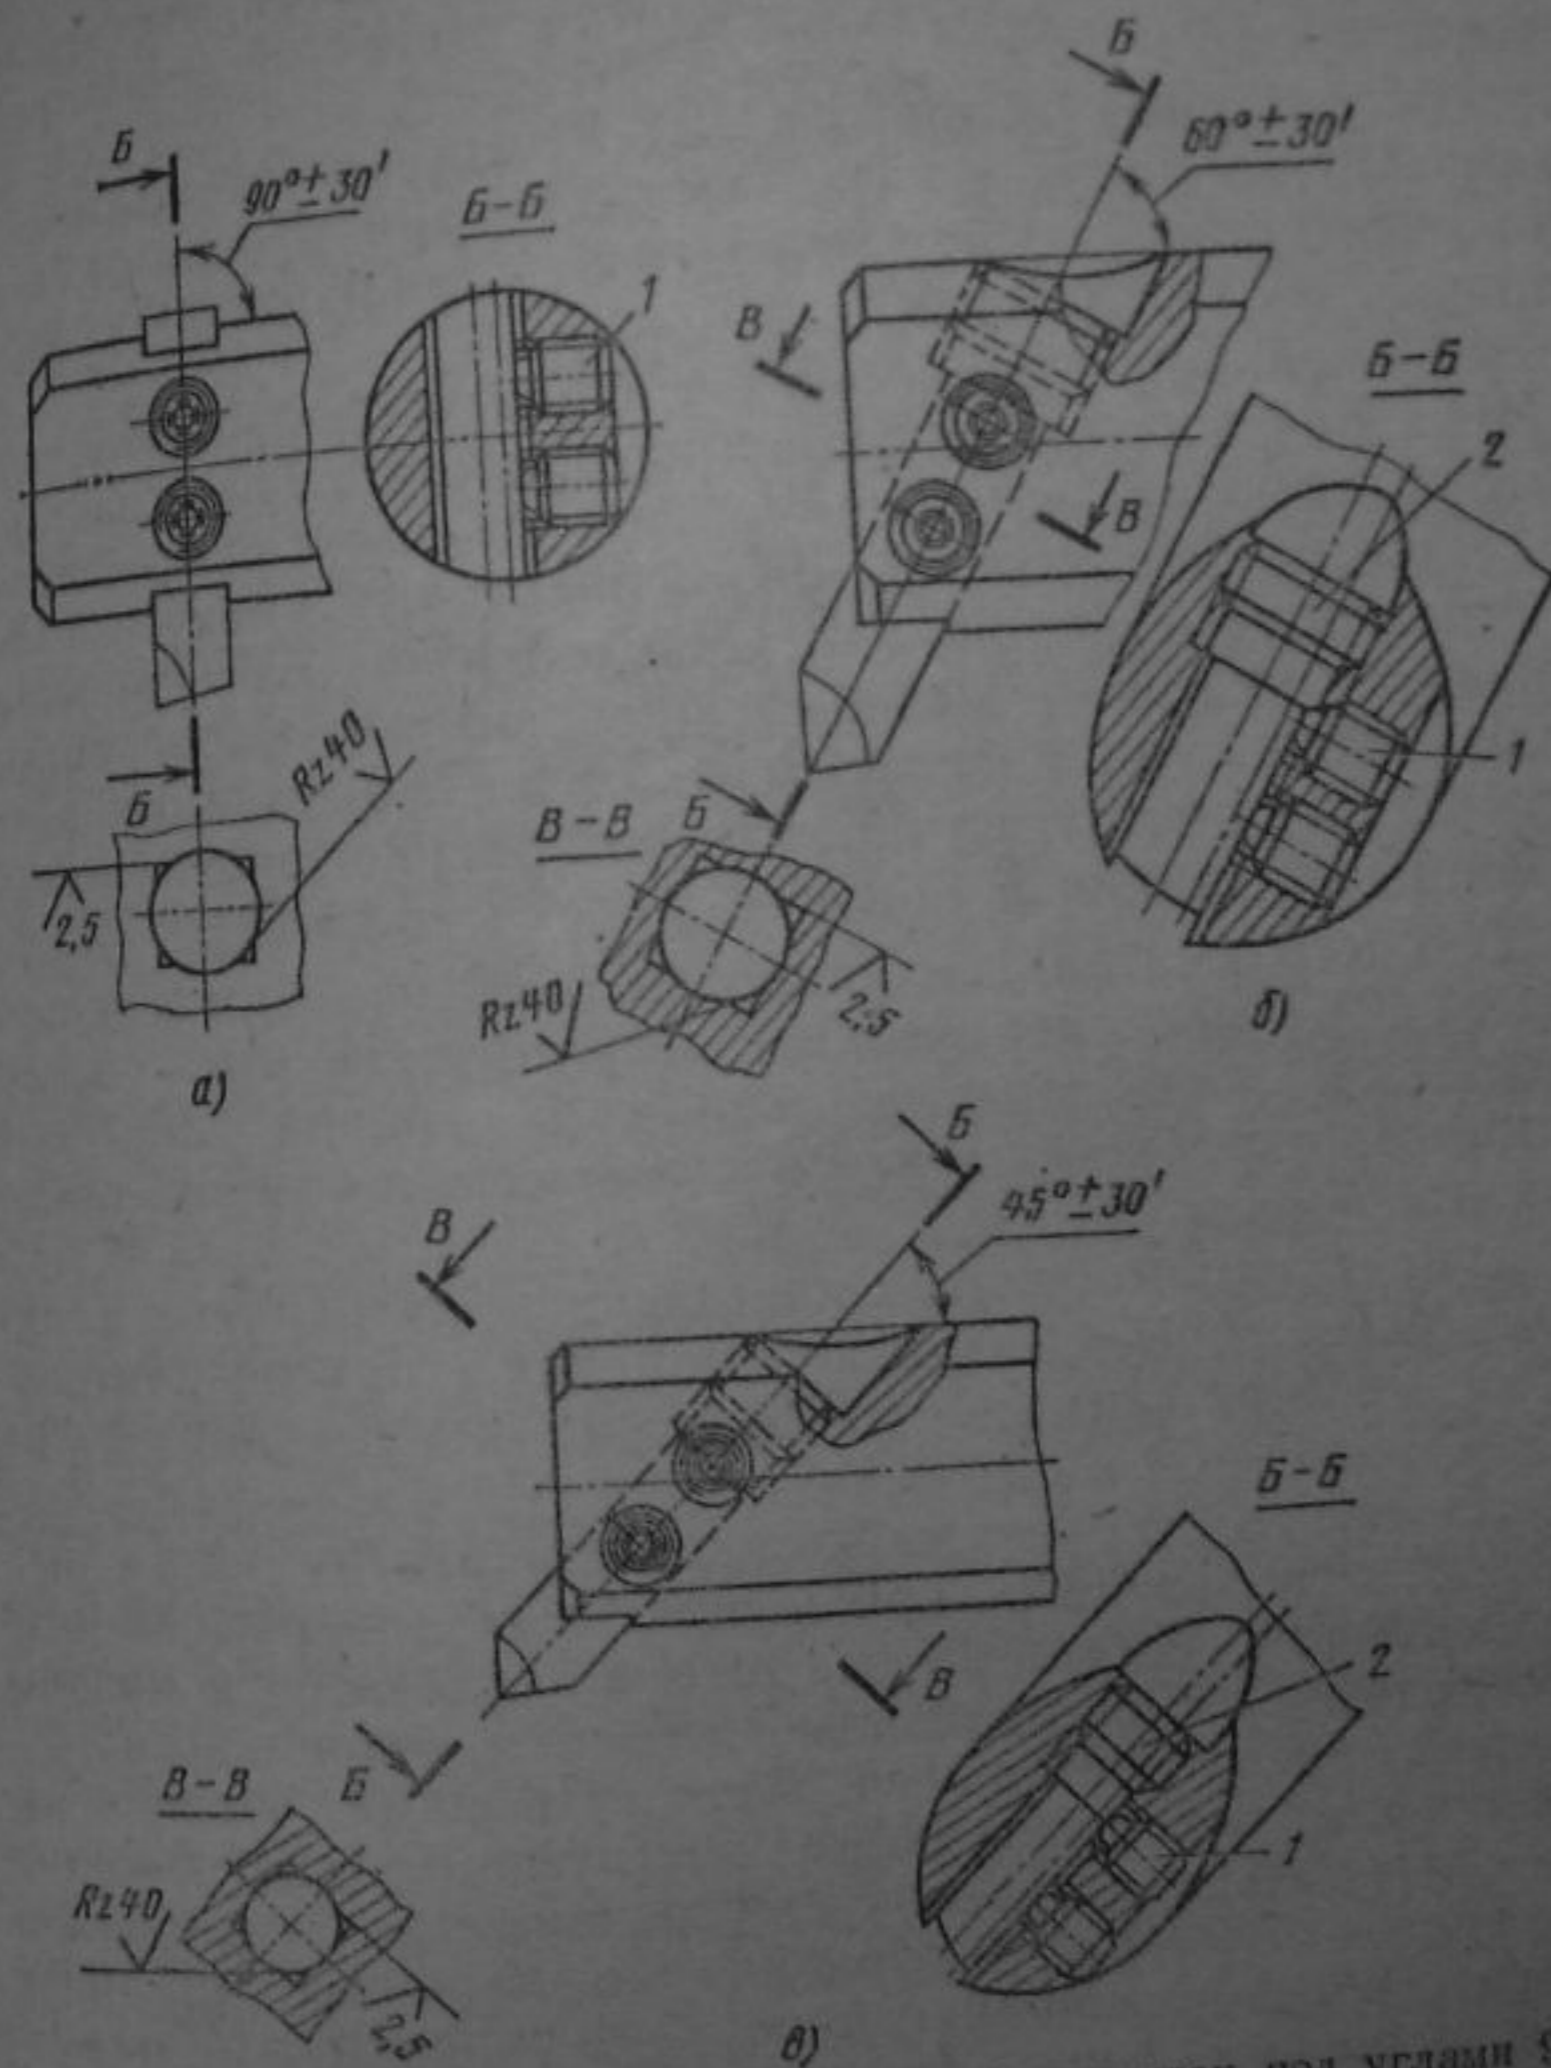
Крепление резца в оправках и борштангах под углами 90, 60 и 45°:
